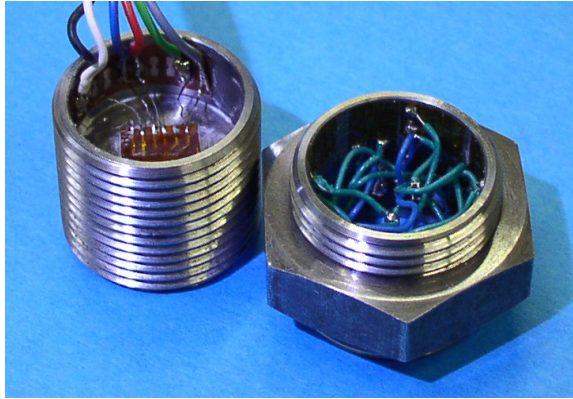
Einschraubbare Sensoren, links mit Membran, rechts als komplett durchbohrte Ausführung mit Kontermutter
